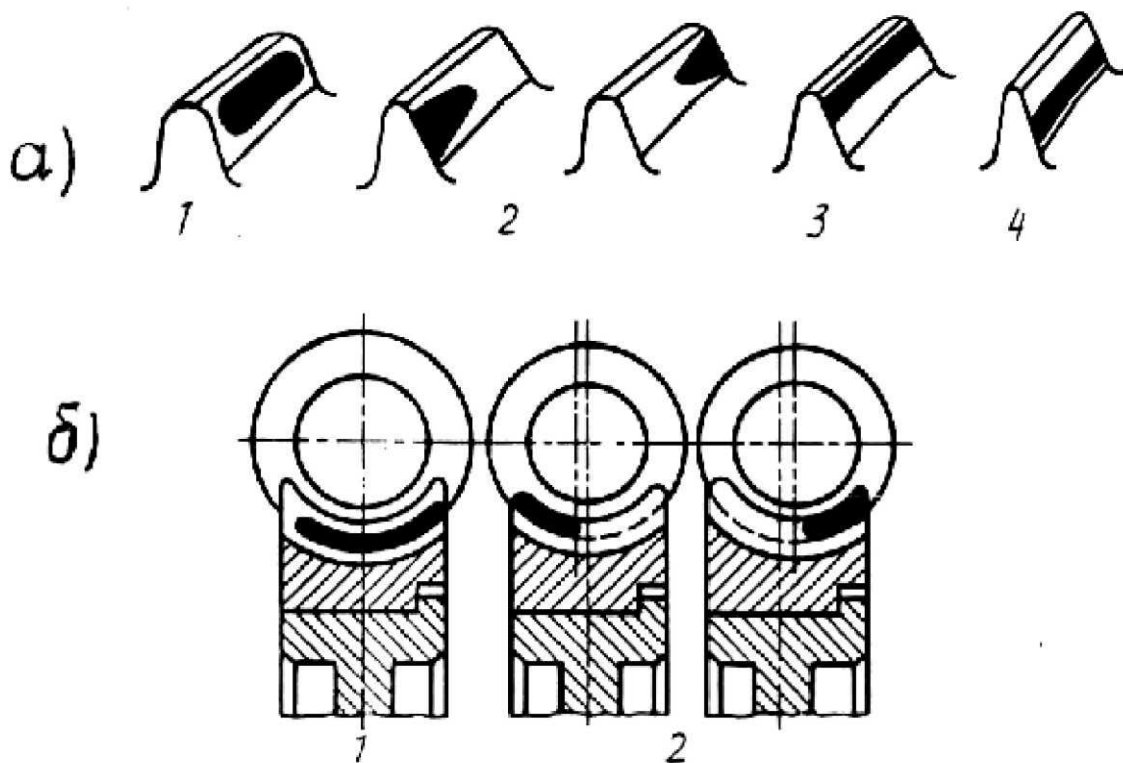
Форма и расположение пятен контакта на поверхности зубьев колес:
